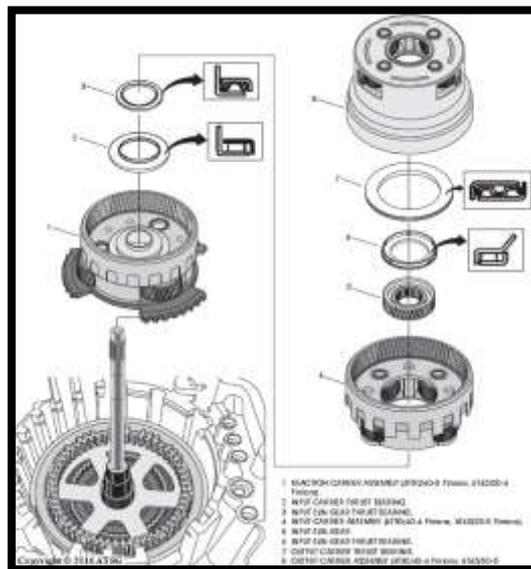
Instalación de engranaje unidireccional (ATSG, 2018)
